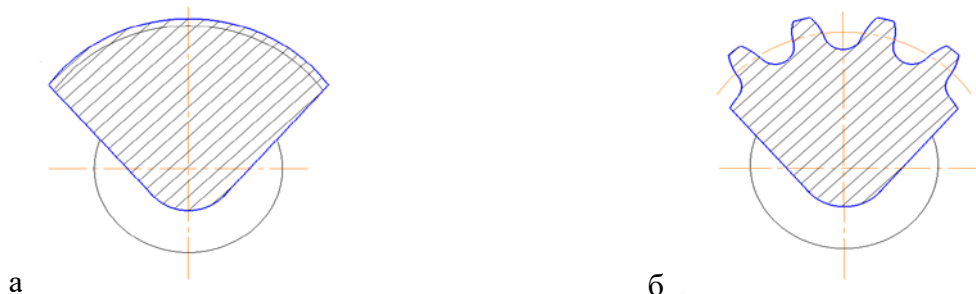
Общий вид поковки зубчатого венца вала сектора 453461.400/002, сталь 25ХГТ.
